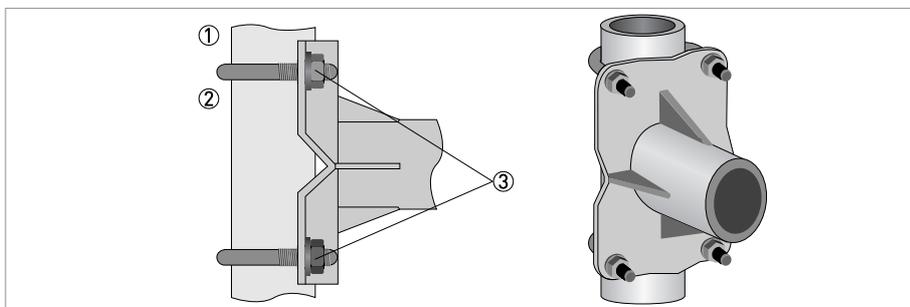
Крепление корпуса конвертера полевой версии
